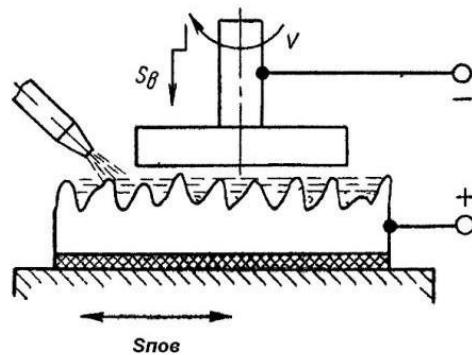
Схема анодно-механічної обробки плоскої поверхні [8]
